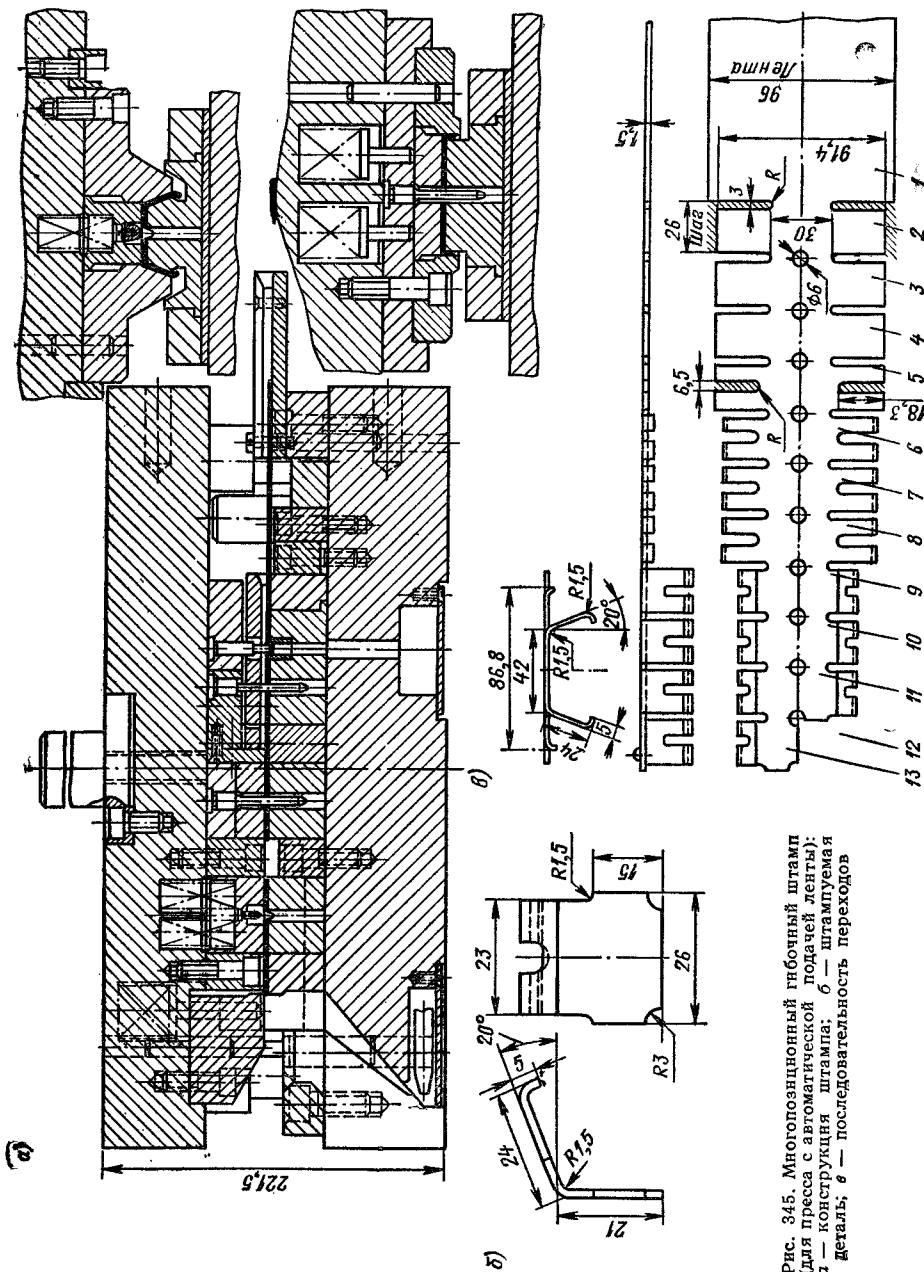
Многопозиционный гибочный штамп (для прессы с автоматической подачей ленты): а — конструкция штампа; б — штампуемая деталь; в — последовательность переходов
